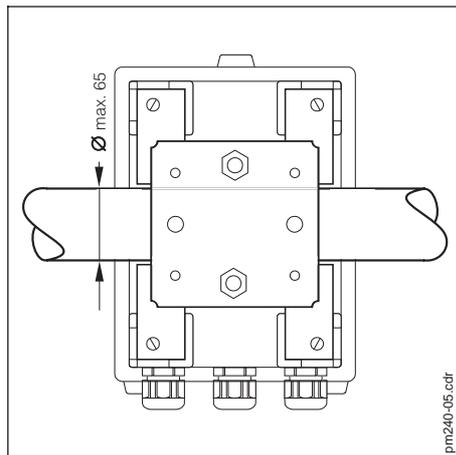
Mastmontage Liquisys CPM 221 mit optionalem Feldgehäuse
